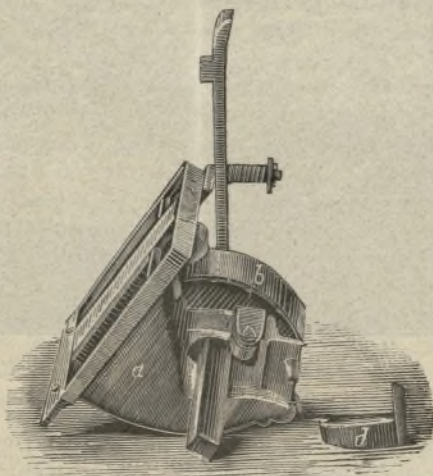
APPARECCHIO DISTRIBUTORE.
